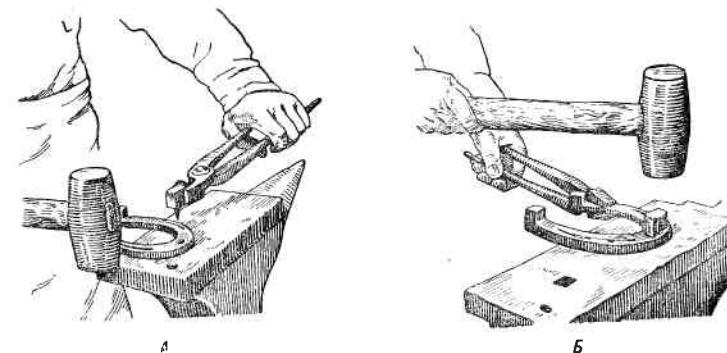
Укрепление зацепного шипа для сварки:
